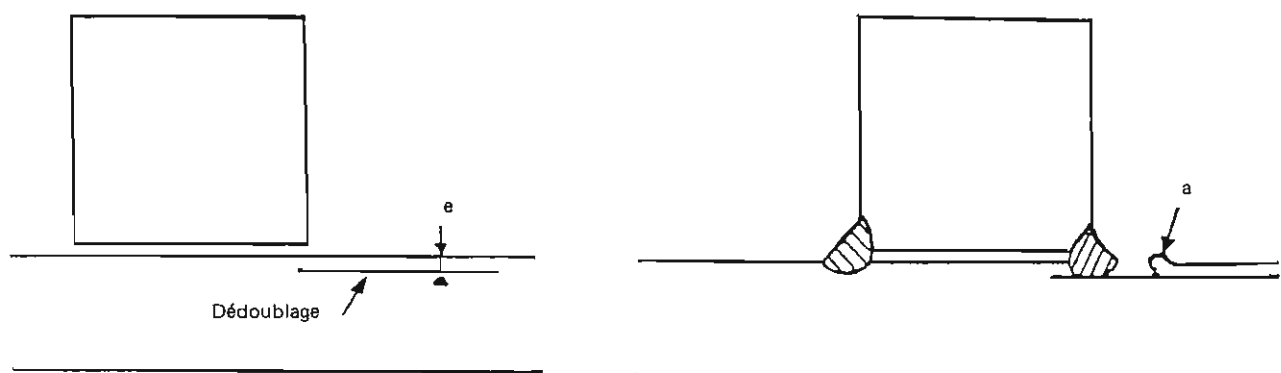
Soudure d'angle - Formation du caniveau
